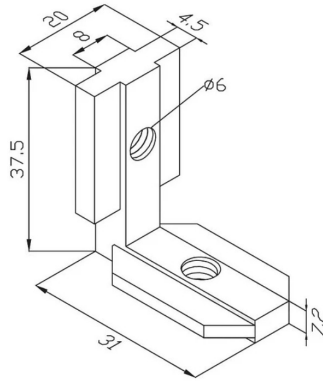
Dimensión de unión ángulo 90° interno 40x40, Fuente: Rmparts
